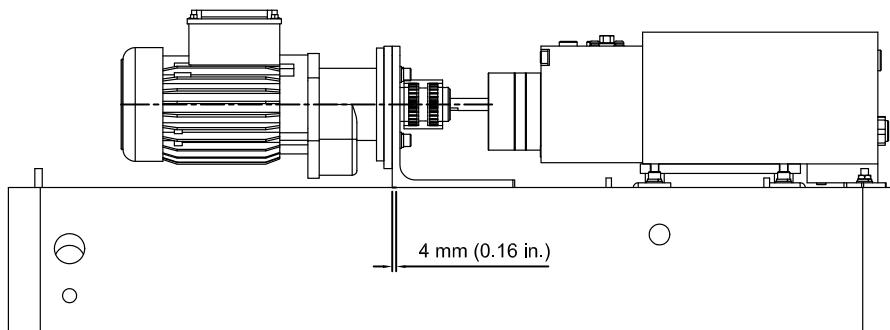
Deslocação do conjunto do motor de 4 mm (0.16 in.)
